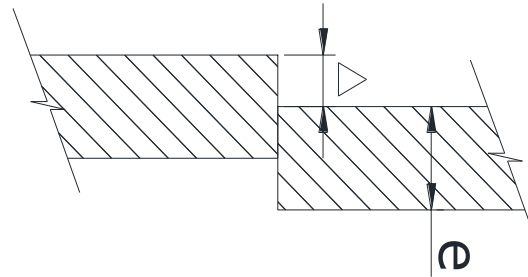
Tolerancia de desalineamiento vertical.
